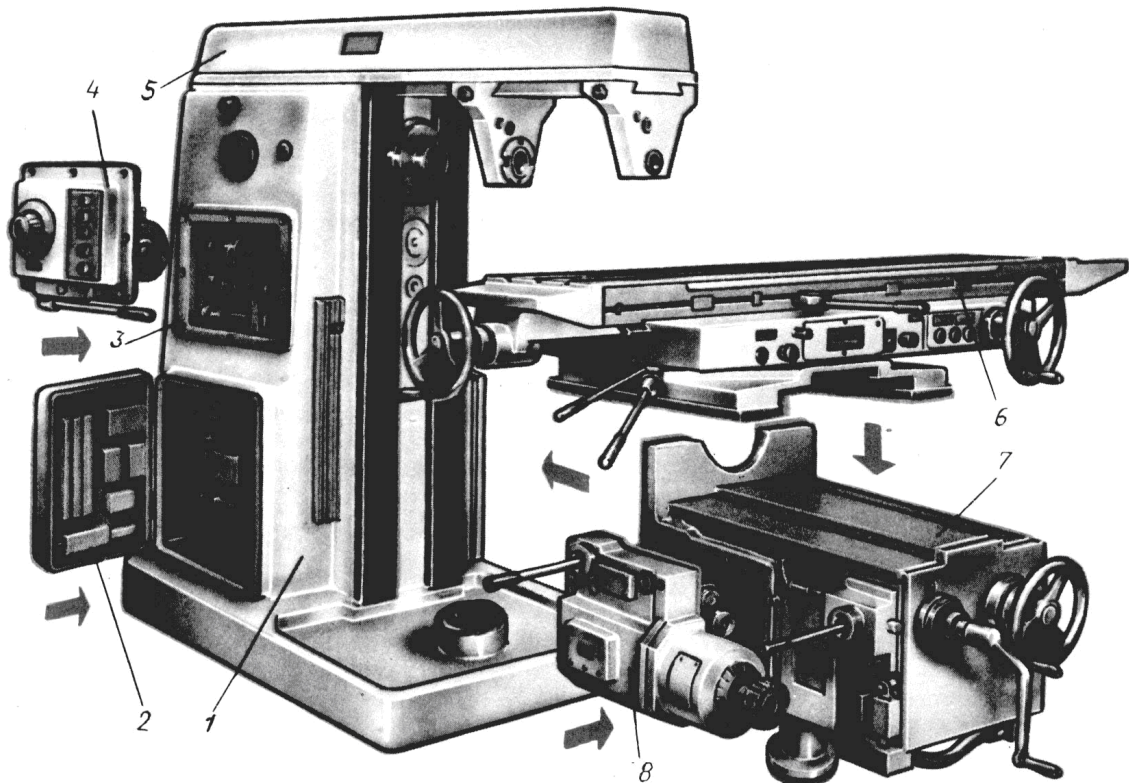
Горизонтально-фрезерний верстат 6P-82
